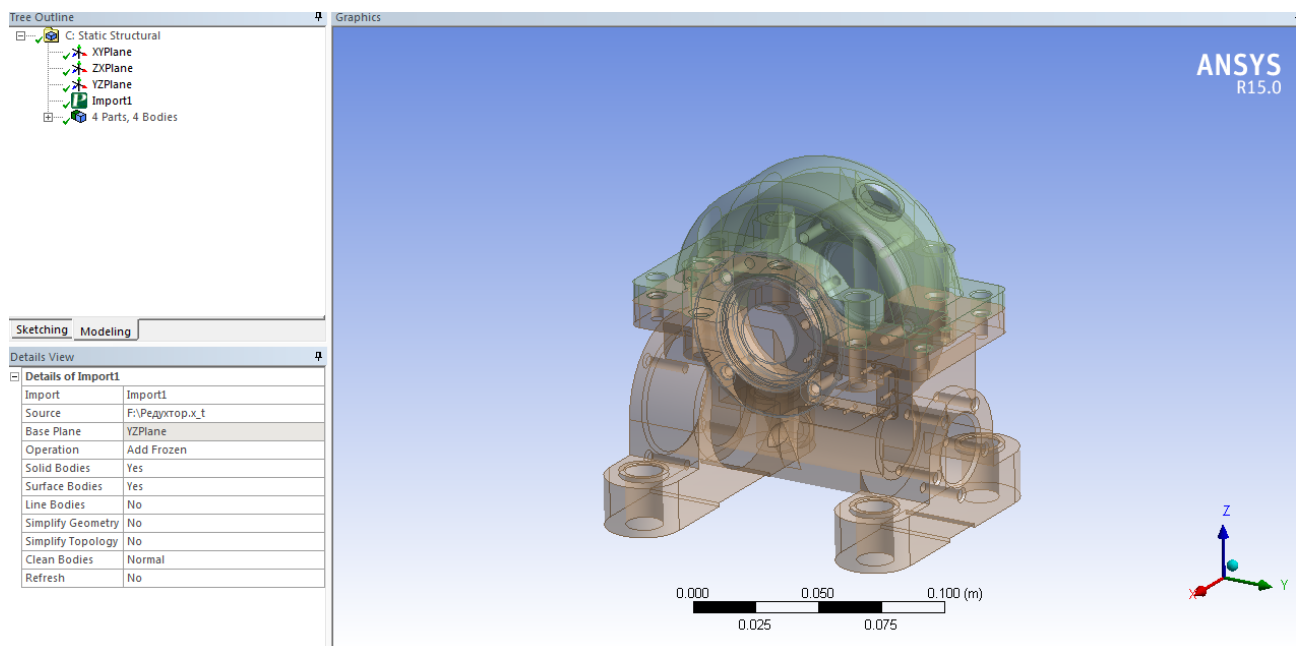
Імпортована геометрія корпусу редуктора
